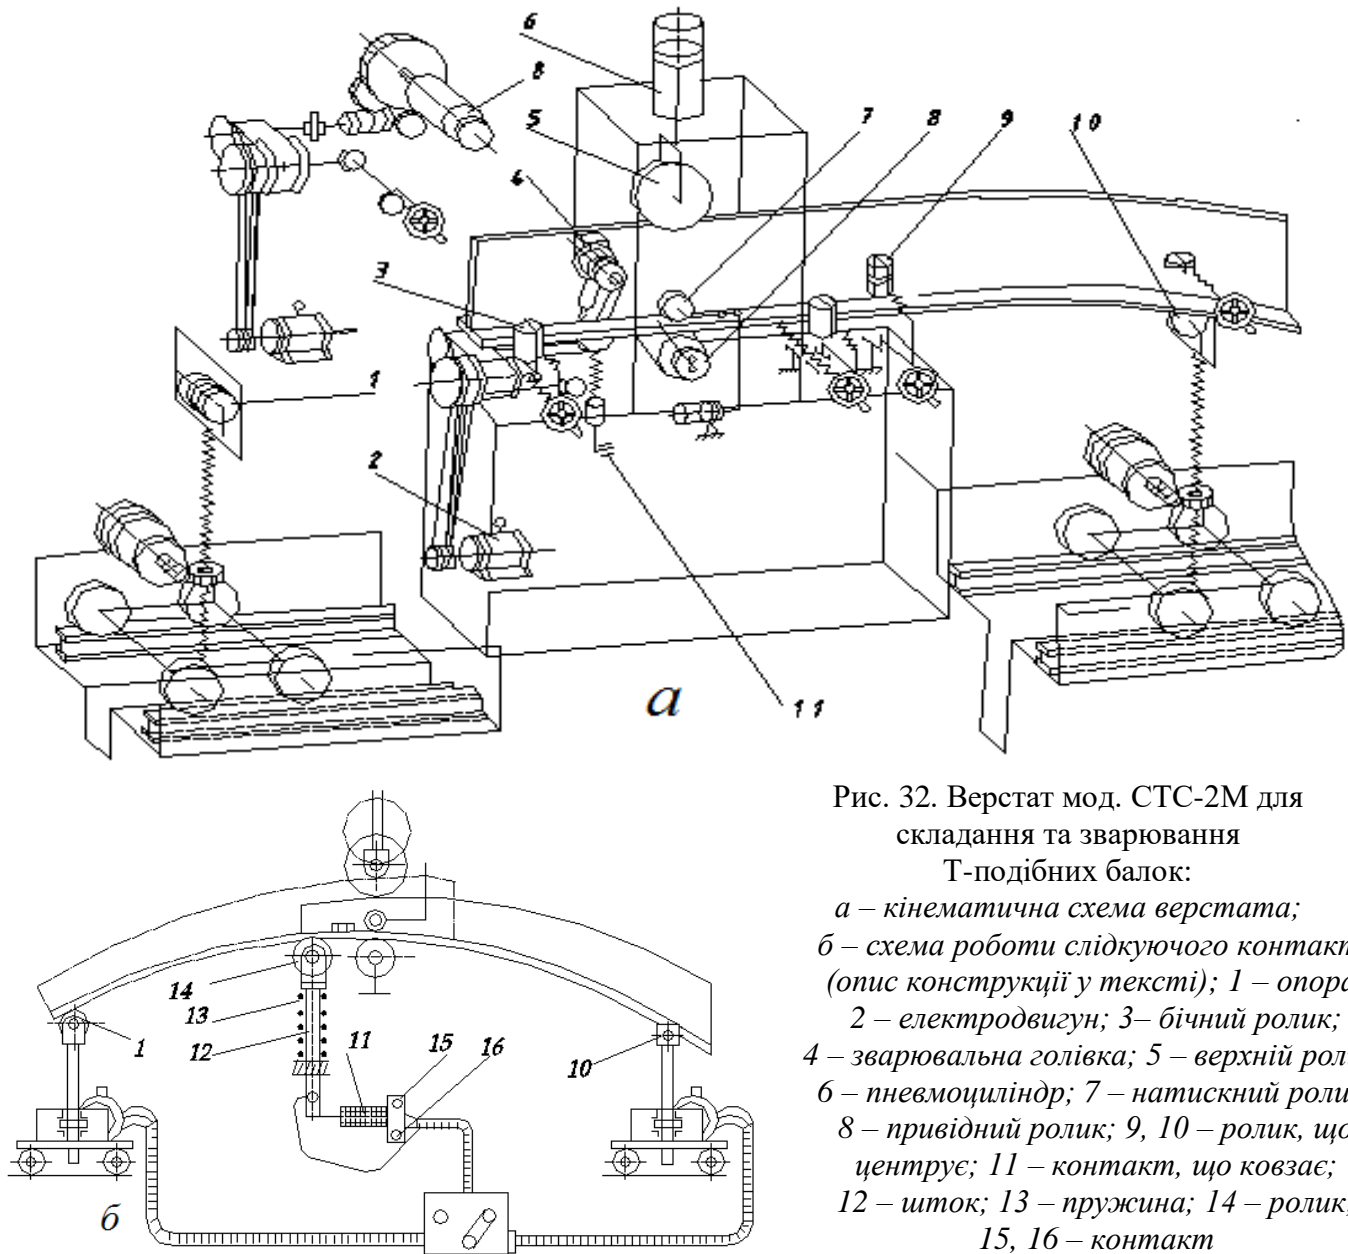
Верстат мод. СТС-2М для складання та зварювання Т-подібних балок:
